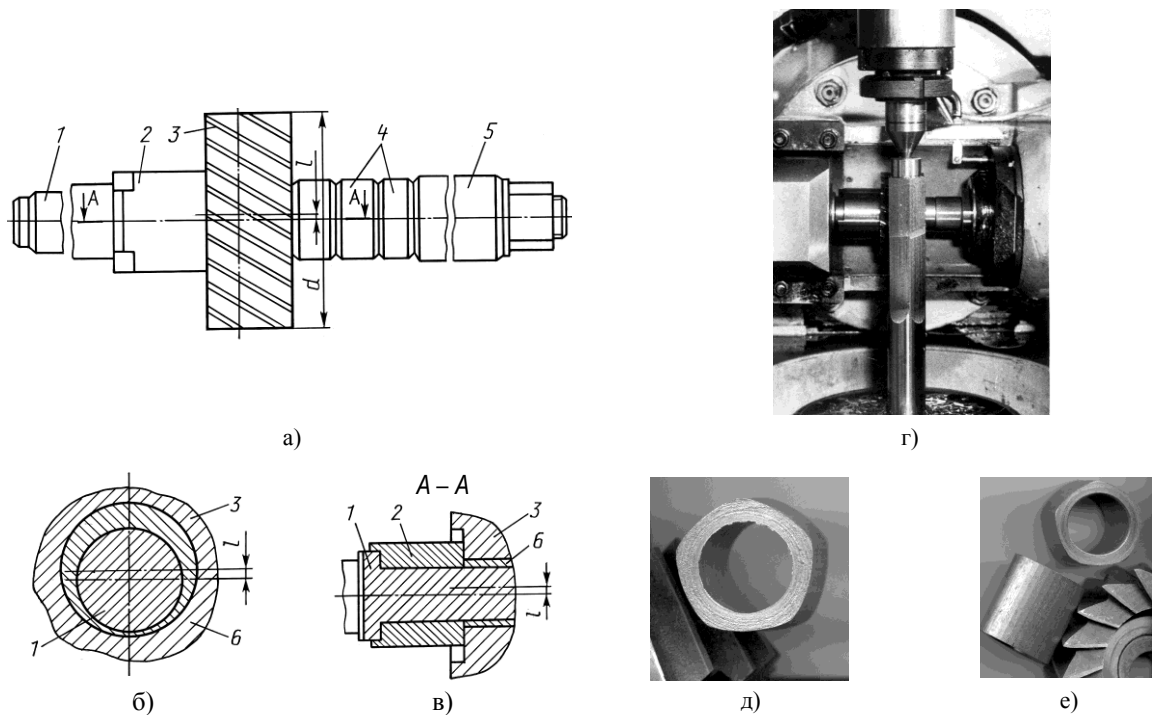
Обработка профильных валов на зубофрезерном станке:
